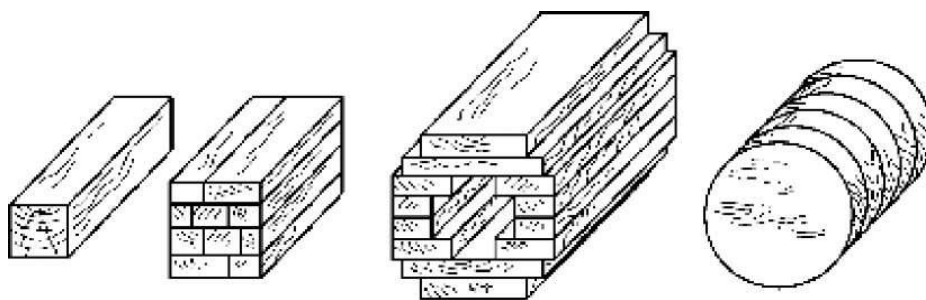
Заготовки для круглых болванок: *a* - цельная; *б* - сплошная клееная; *в* - клееная полая; *г* - клееная из дисков
